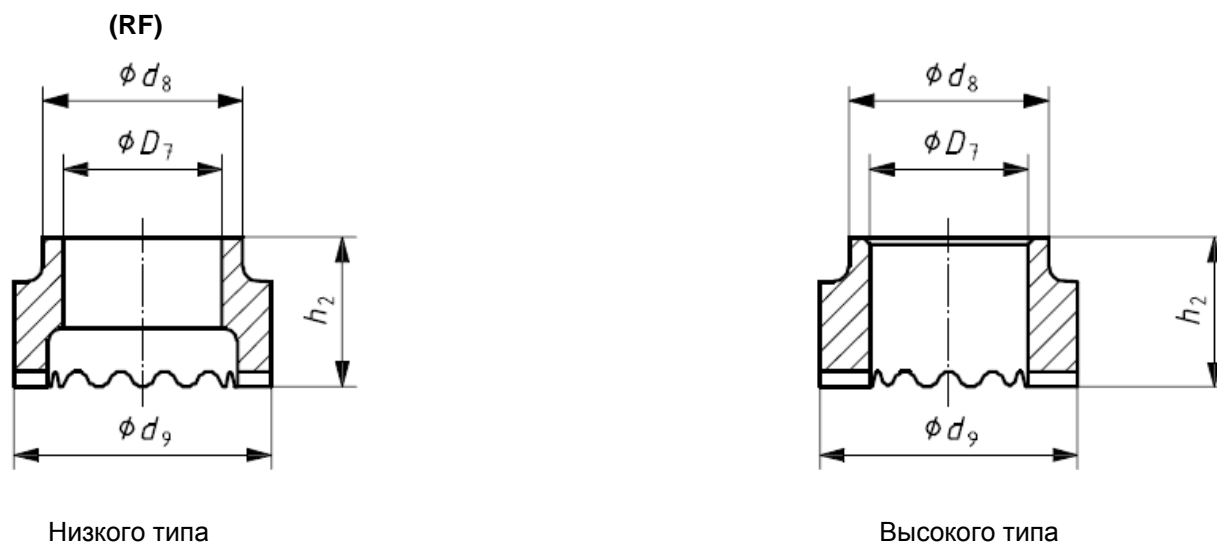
Керамическое кольцо для шпильки с резьбой с редуцированным стержнем (RF)
